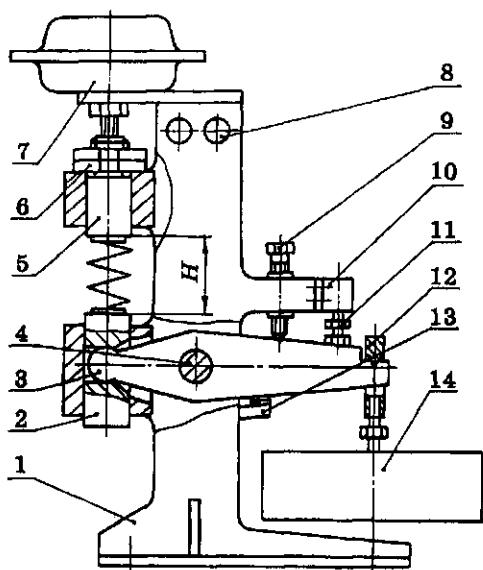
Стенд для контроля жесткости пружин: 1 — корпус; 2, 5 — скалки; 3 — рычаг; 4 — ось; 6 — гайки регулировочные; 7 — пневмокамера; 8 — световой индикатор; 9 и 11 — болты регулировочные; 10 — конечный выключатель; 12 — призма; 13 — упор; 14 — груз
